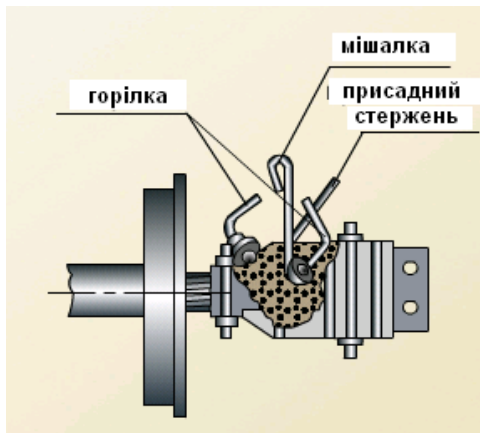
Окінювання алюмінієвих жил пластинами з використанням газової зварки
